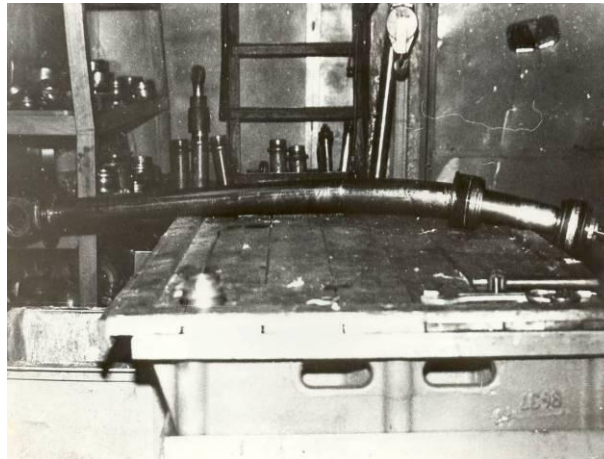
Изгиб штока гидроцилиндра рукояти одноковшового экскаватора
